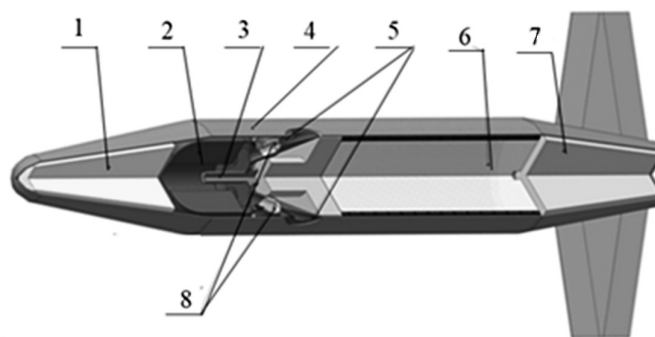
Компоновка МУР БД: 1 — неконтактный датчик цели; 2 — заряд твердого топлива; 3 — воспламенитель; 4 — корпус; 5 — сопло; 6 — боевая часть; 7 — приборы управления; 8 — клапан регулирования тяги
